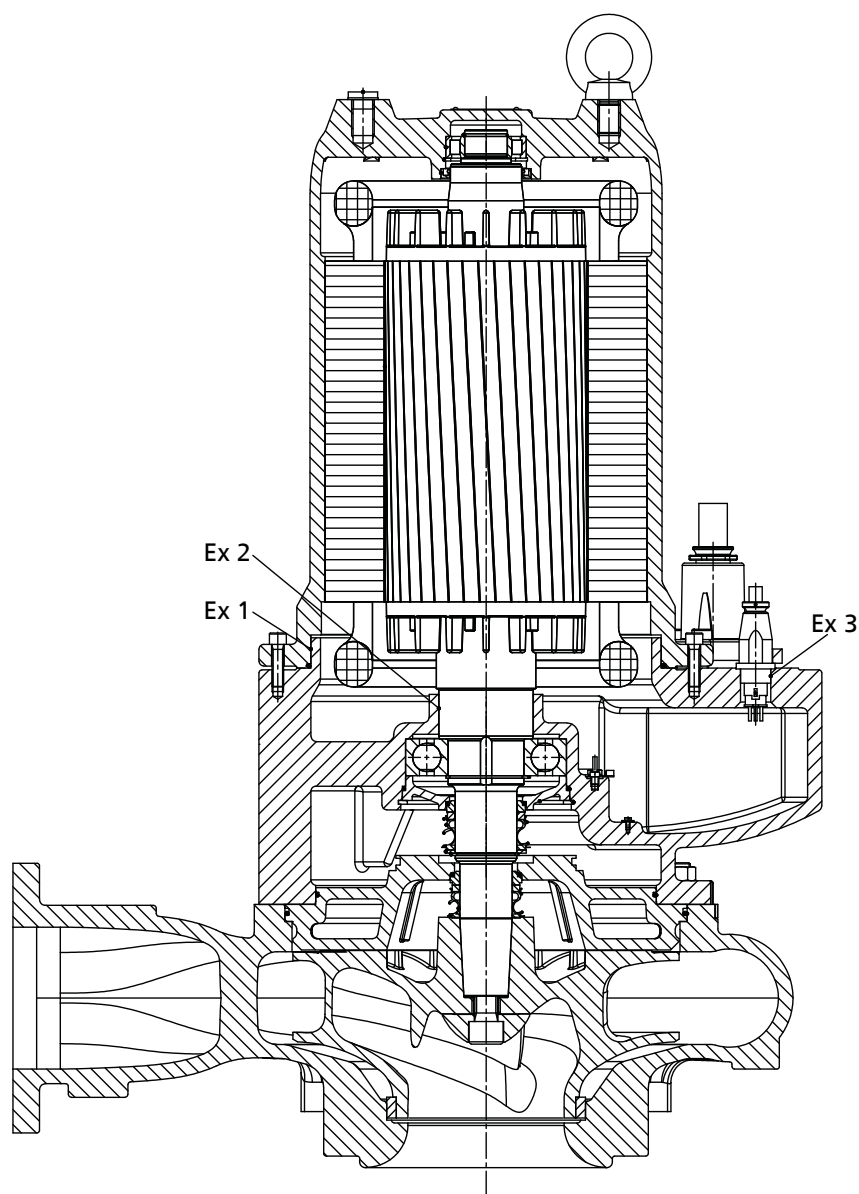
Поверхности взрывозащитных зазоров Amarex KRT, тип двигателя 3
